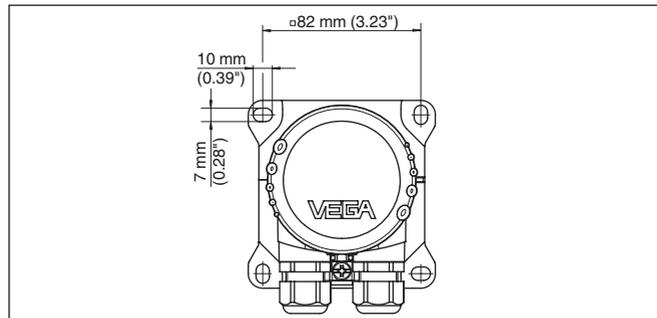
Medida de taladro VEGABOX 03 para montaje mural
